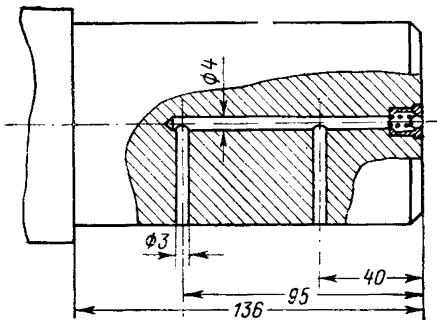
Установка прессмасленок типа V-2Б для смазки осей колес
